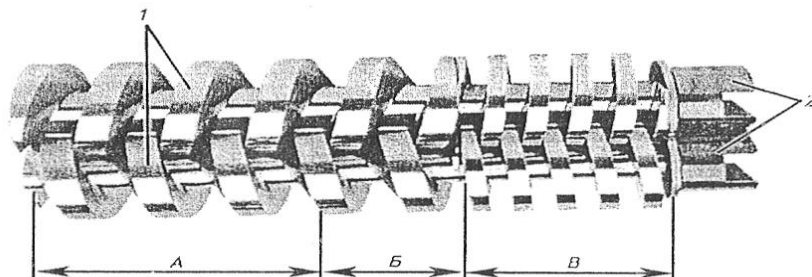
Здвоєні шнеки шнекового витиснювача:
